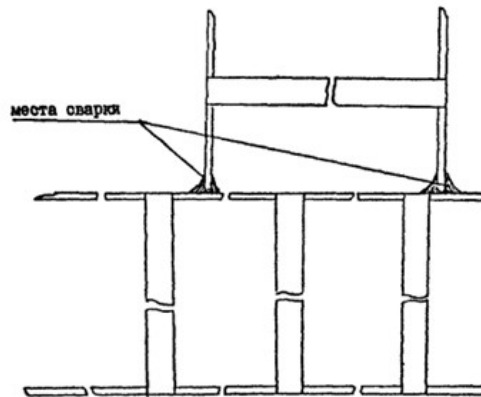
Сварка конструкций из полосового металла при стыке в 90° . Угольники срачиваются методом сварки в стык (рис.18а) или внахлест (рис.11).
